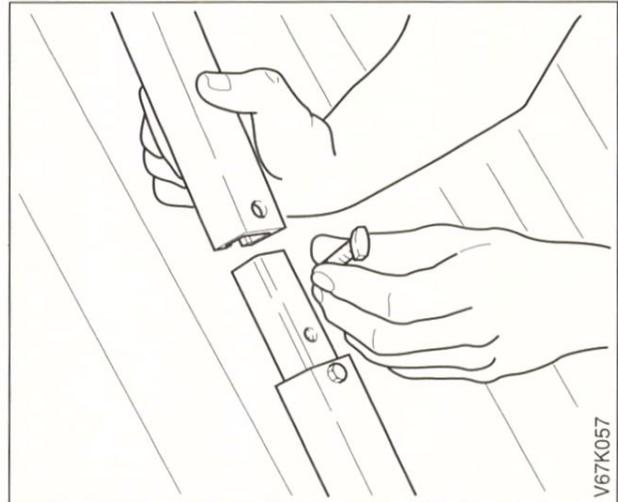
Montageschienen mit Kupplung zusammensetzen und Hammerkopfschrauben (M8x50) mit Muttern sowie Unterlegscheiben locker aufdrehen.
